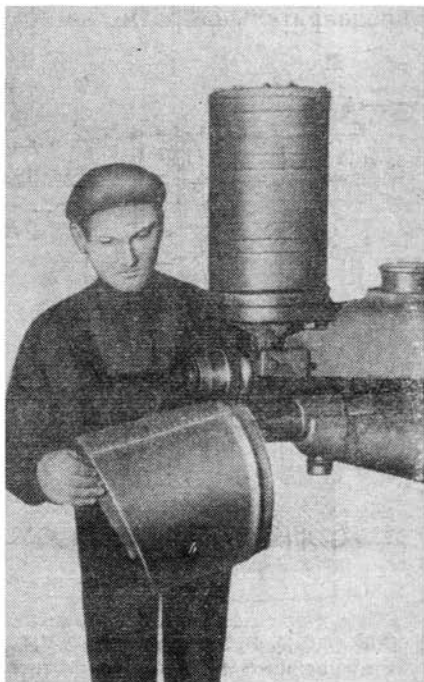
Рабочий момент изготовления на зигмашине ЗМ-4 гофра и валика жесткости на звене воздуховода круглого сечения
